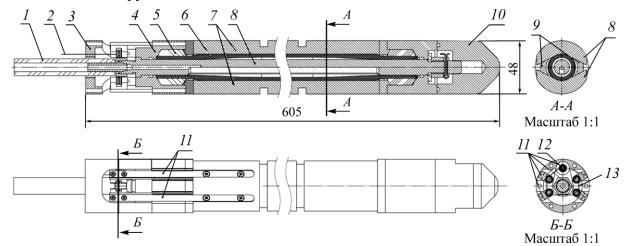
Общий вид скважинного прибора: I — рукав высокого давления; 2 — сигнальный электрический кабель; 3 — корпус измерительного узла; 4 — цилиндр; 5 — упругий элемент; 6 — резиновая трубка; 7 — контактный элемент; 8 — стержень; 9 — пуансон; 10 — защитный кожух; 11 — планка; 12 — энкодер (датчик угла поворота); 13 — лента; 14 — клипса
